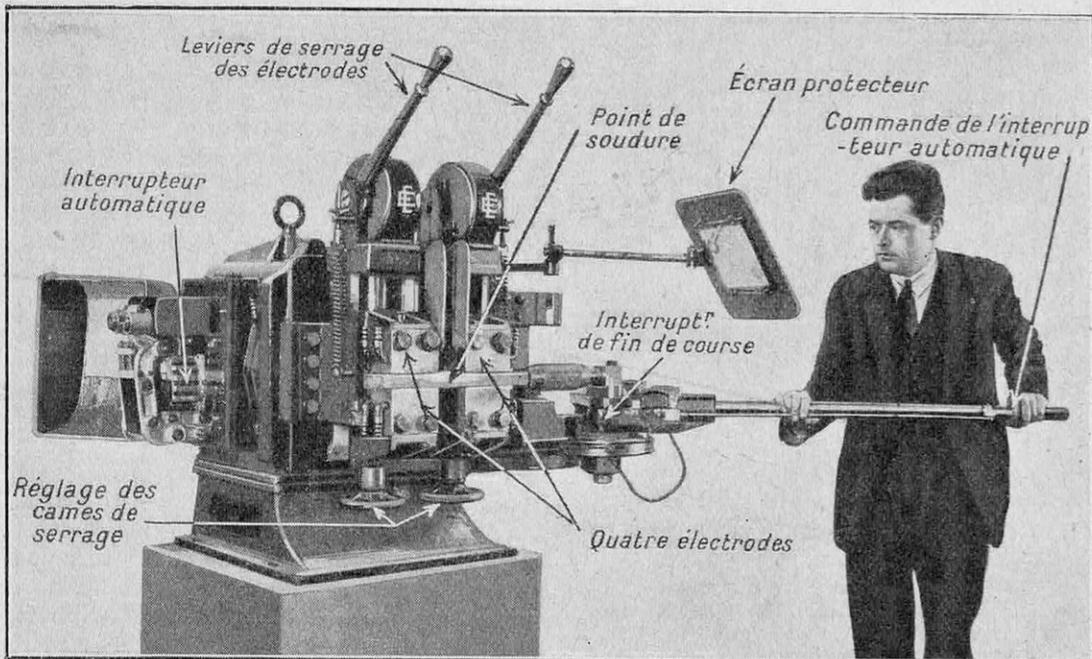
LA MACHINE ÉLECTRIQUE A SOUDER PAR BOUTS DE L'ÉLECTRO-OUTILLAGE
